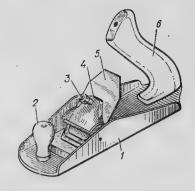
1 — колодка; 2 — рукоятка; 3 — винт прижимной; 4 прижим; 5 — нож; 6 — ручка
